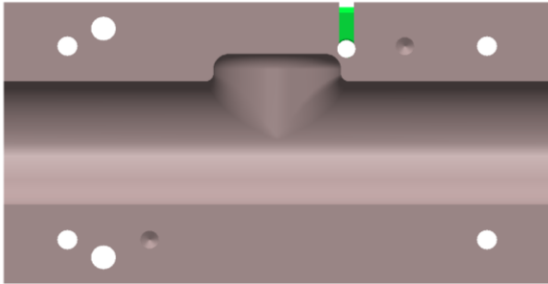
Umformwerkzeug Obergesenk mit Bohrung (grün) für den Sensorstift.
